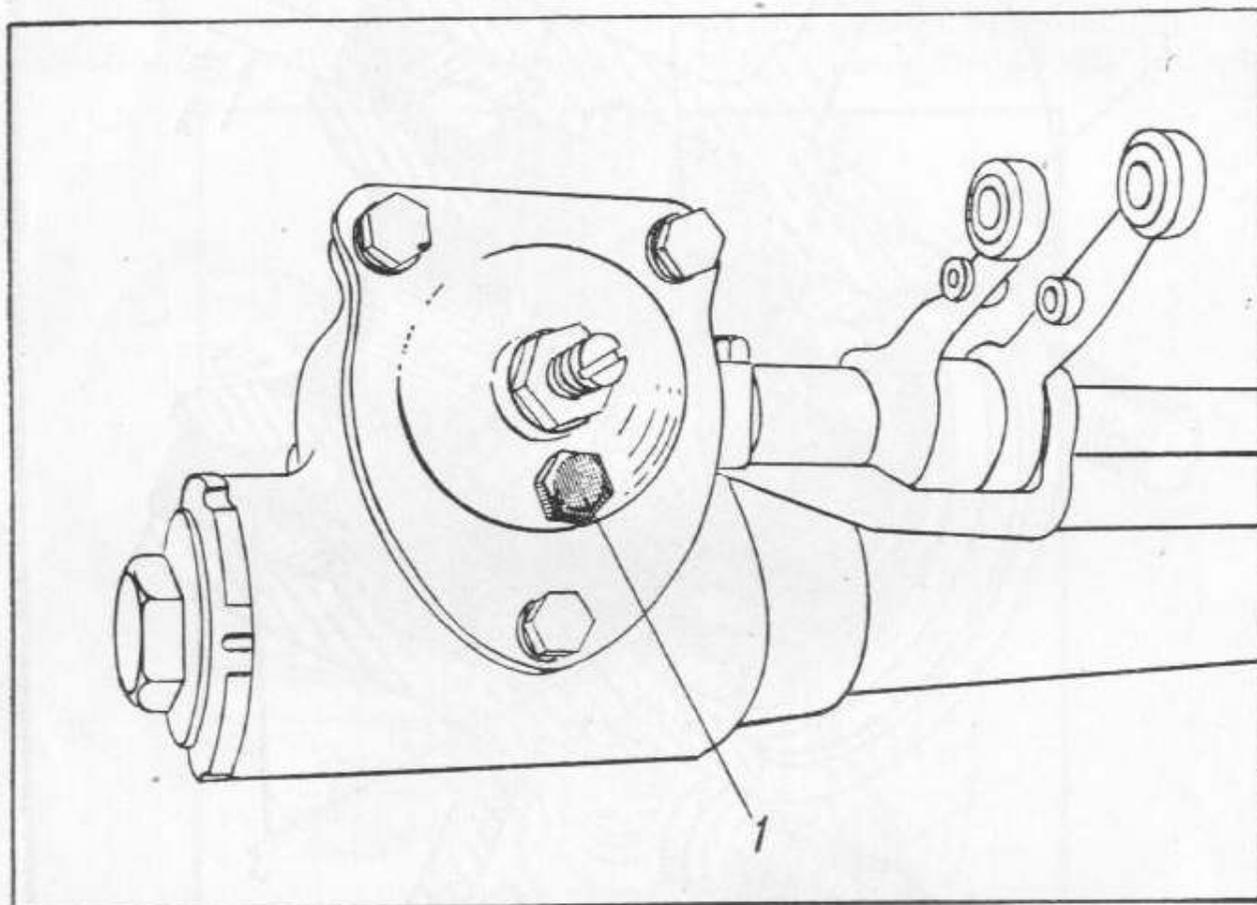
Anordnung der Verschlussschraube an Einfüllöffnung des Lenkgehäuses
